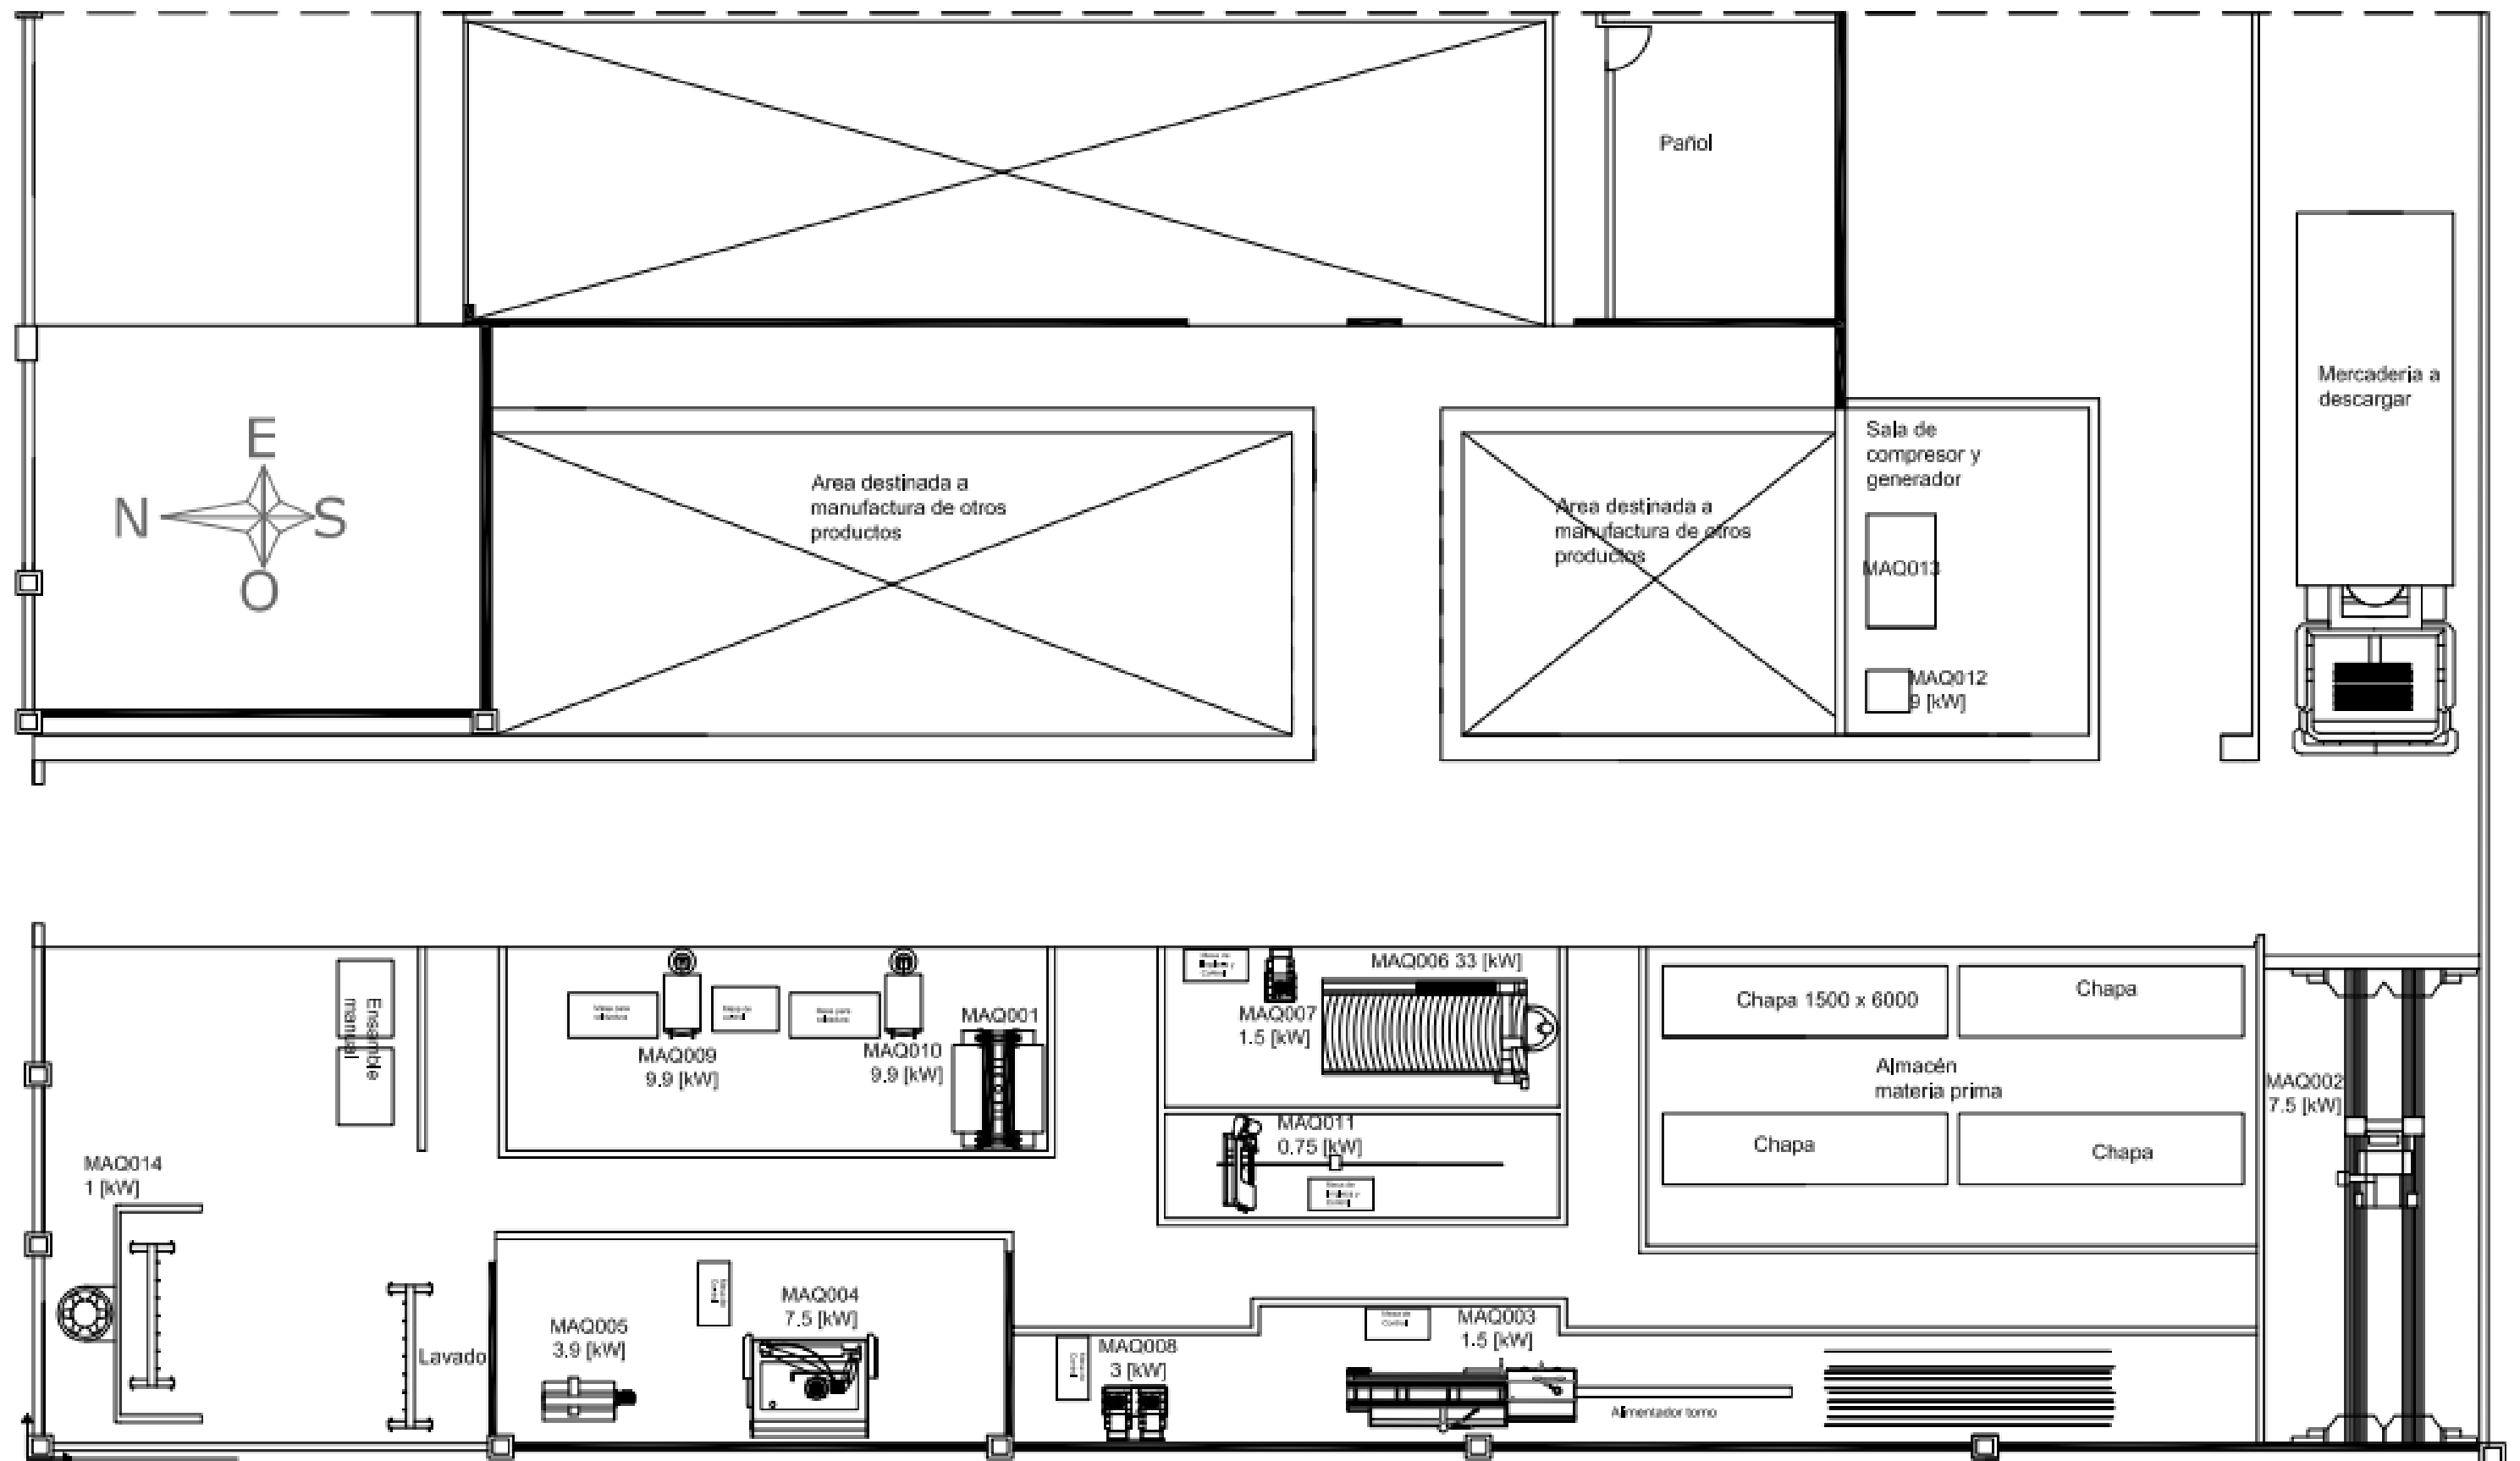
Layout de planta con ubicación de máquinas. Elaboración propia.
